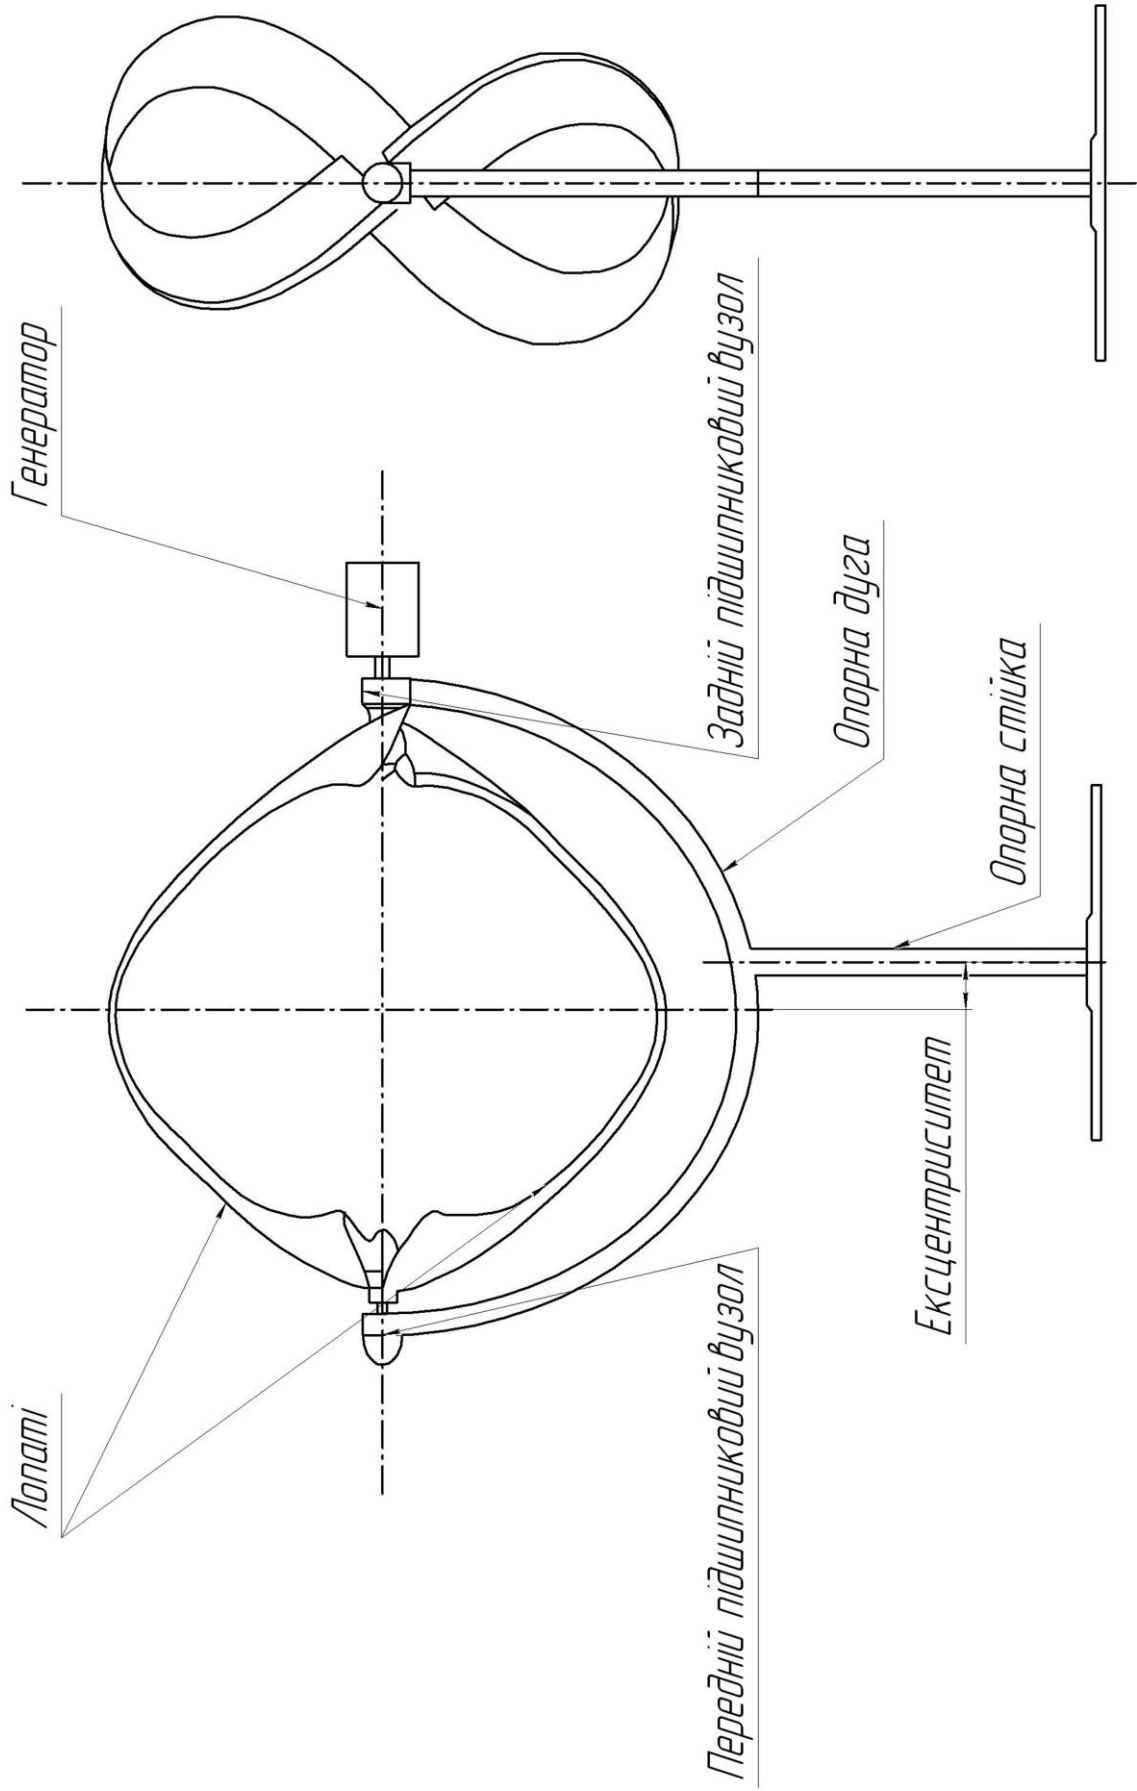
Загальний вид вітроагрегата зі спіральними лопатями
